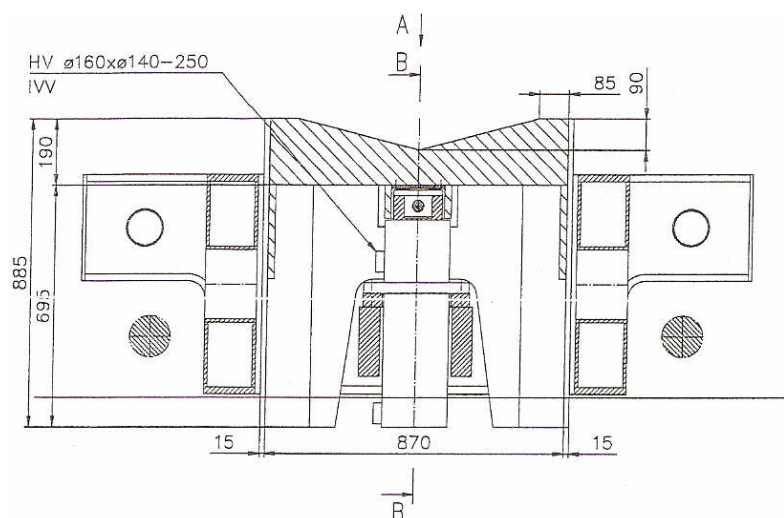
Konstrukce vozíku (foto z výkresu KLL s.r.o.)
